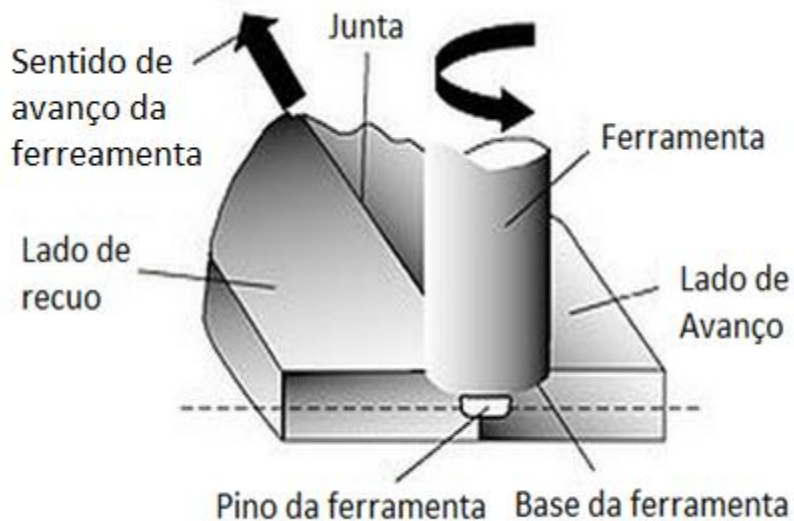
Soldadura por *friction stir welding* (FSW)
